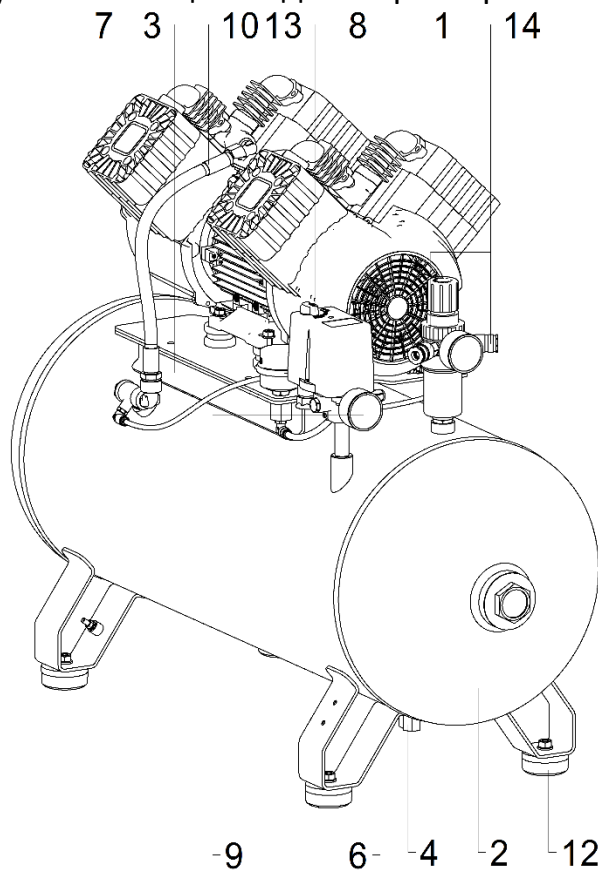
Общий вид компрессора СБ4/Ф-100.4V55
